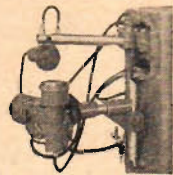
Sömsvetsmaskin typ SVS 533 med fixtur för svetsning av flottörer.
